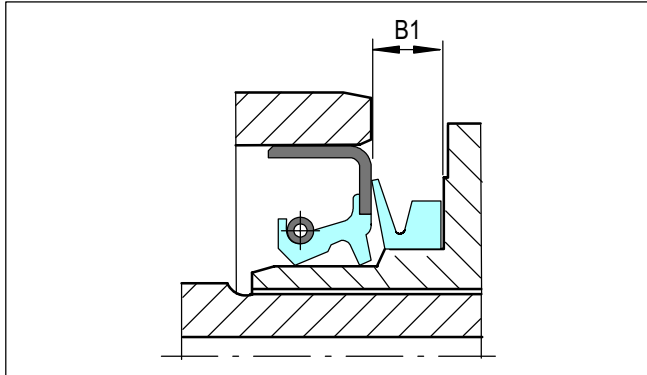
Pierścień V-ring zamontowany na końcówce wału
